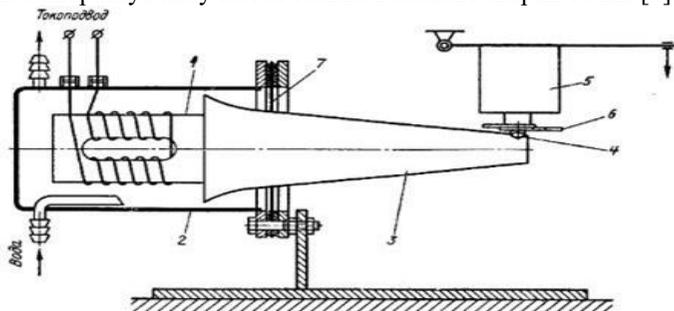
Схема установки для точечной (прессовой) сварки ультразвуком состоит из [5]: 1 - электрохимического преобразователя с обмотками, заключенного в металлический корпус 2, охлаждаемый водой; 3 - трансформатора упругих колебаний; 4 - сварочного наконечника; опоры с механизмом давления 5 и свариваемых деталей 6. Крепление колебательной системы производят с помощью диафрагмы 7.
